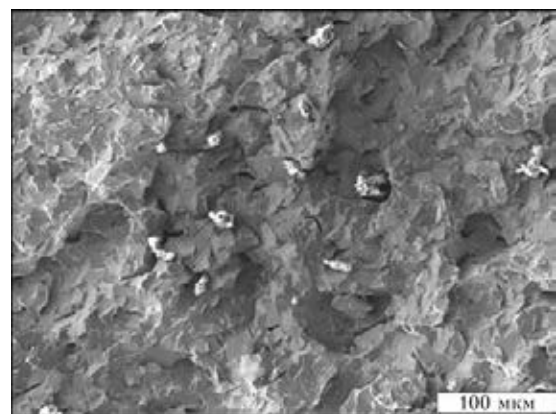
Тугоплавкие неметаллические включения на поверхности излома сварного соединения рельсов
